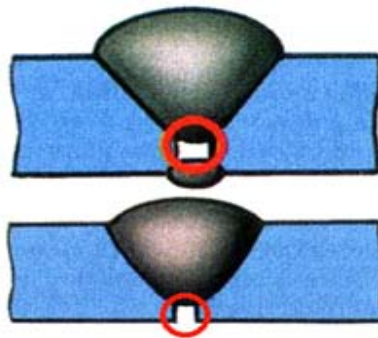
Дефект зварного з'єднання непровар
